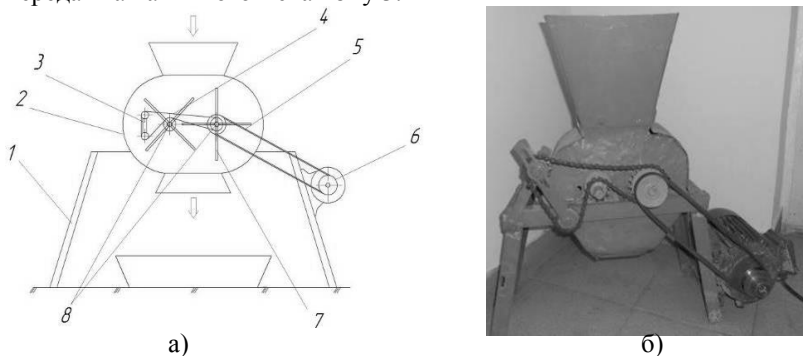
Схема (а) та загальний вигляд (б) пристрою для подрібнення частинок сапропелевих добрив: 1 - корпус; 2 - кожух; 3 - натяжний пристрій; 4 - ланцюгова передача; 5 - пасова передача; 6 - двигун; 7 - лопаті; 8 - ротор
